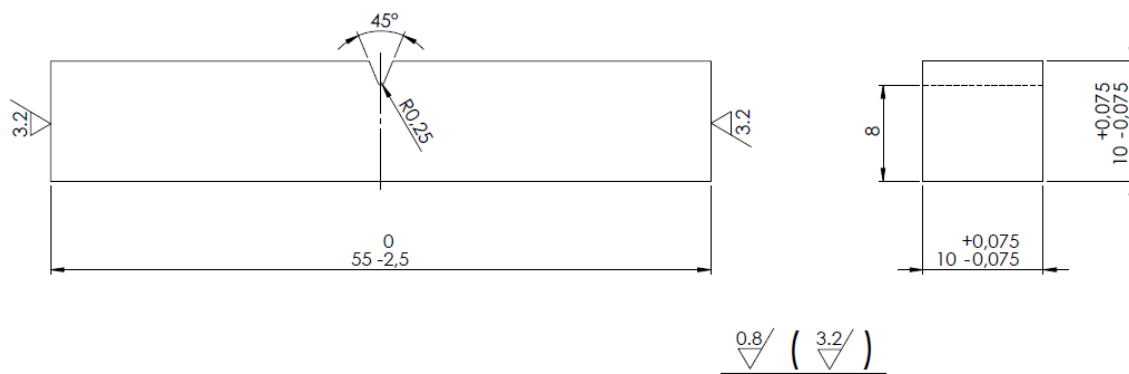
Dimensionamento do corpo de prova para o ensaio mecânico de impacto (charpy) – adaptado da norma ASTM E23
